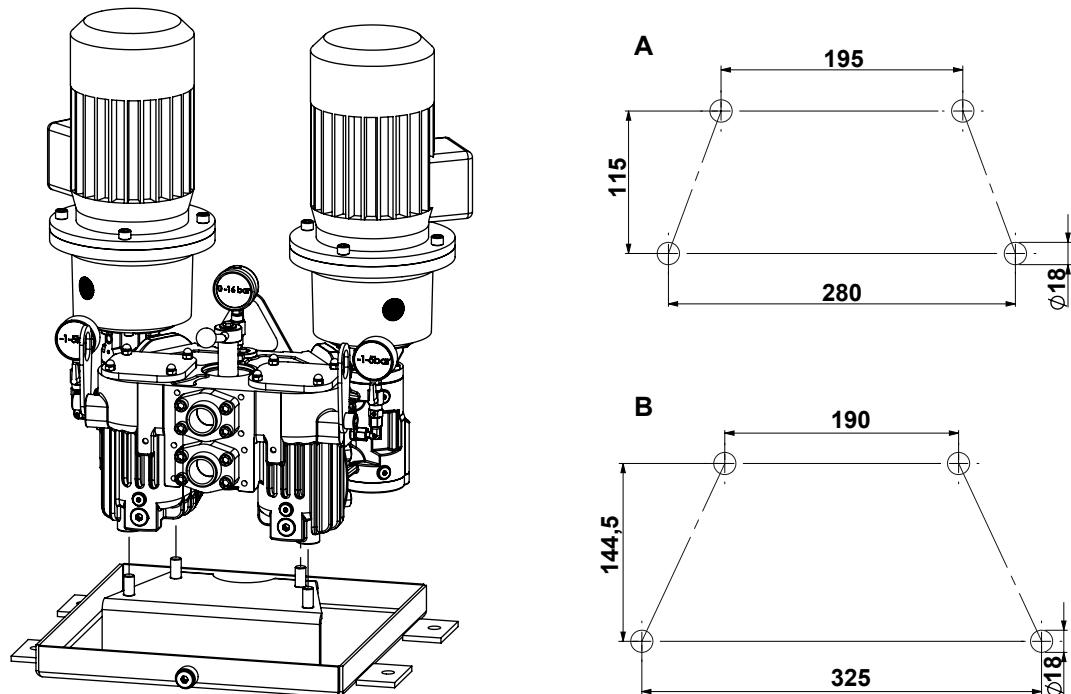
Montage auf Grundrahmen mit Ölwanne
